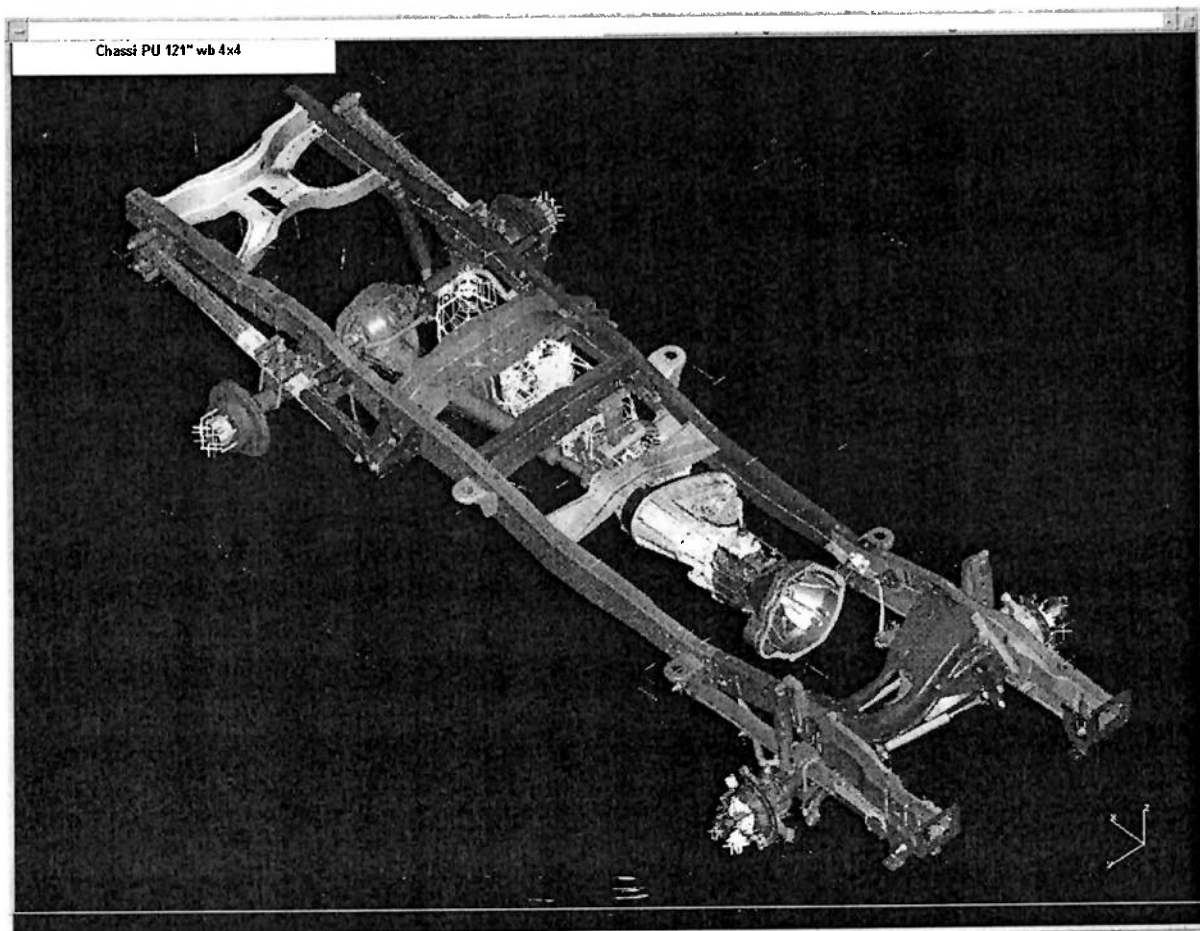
Chassi PU 121”wb 4x4 – Vista Isométrica
